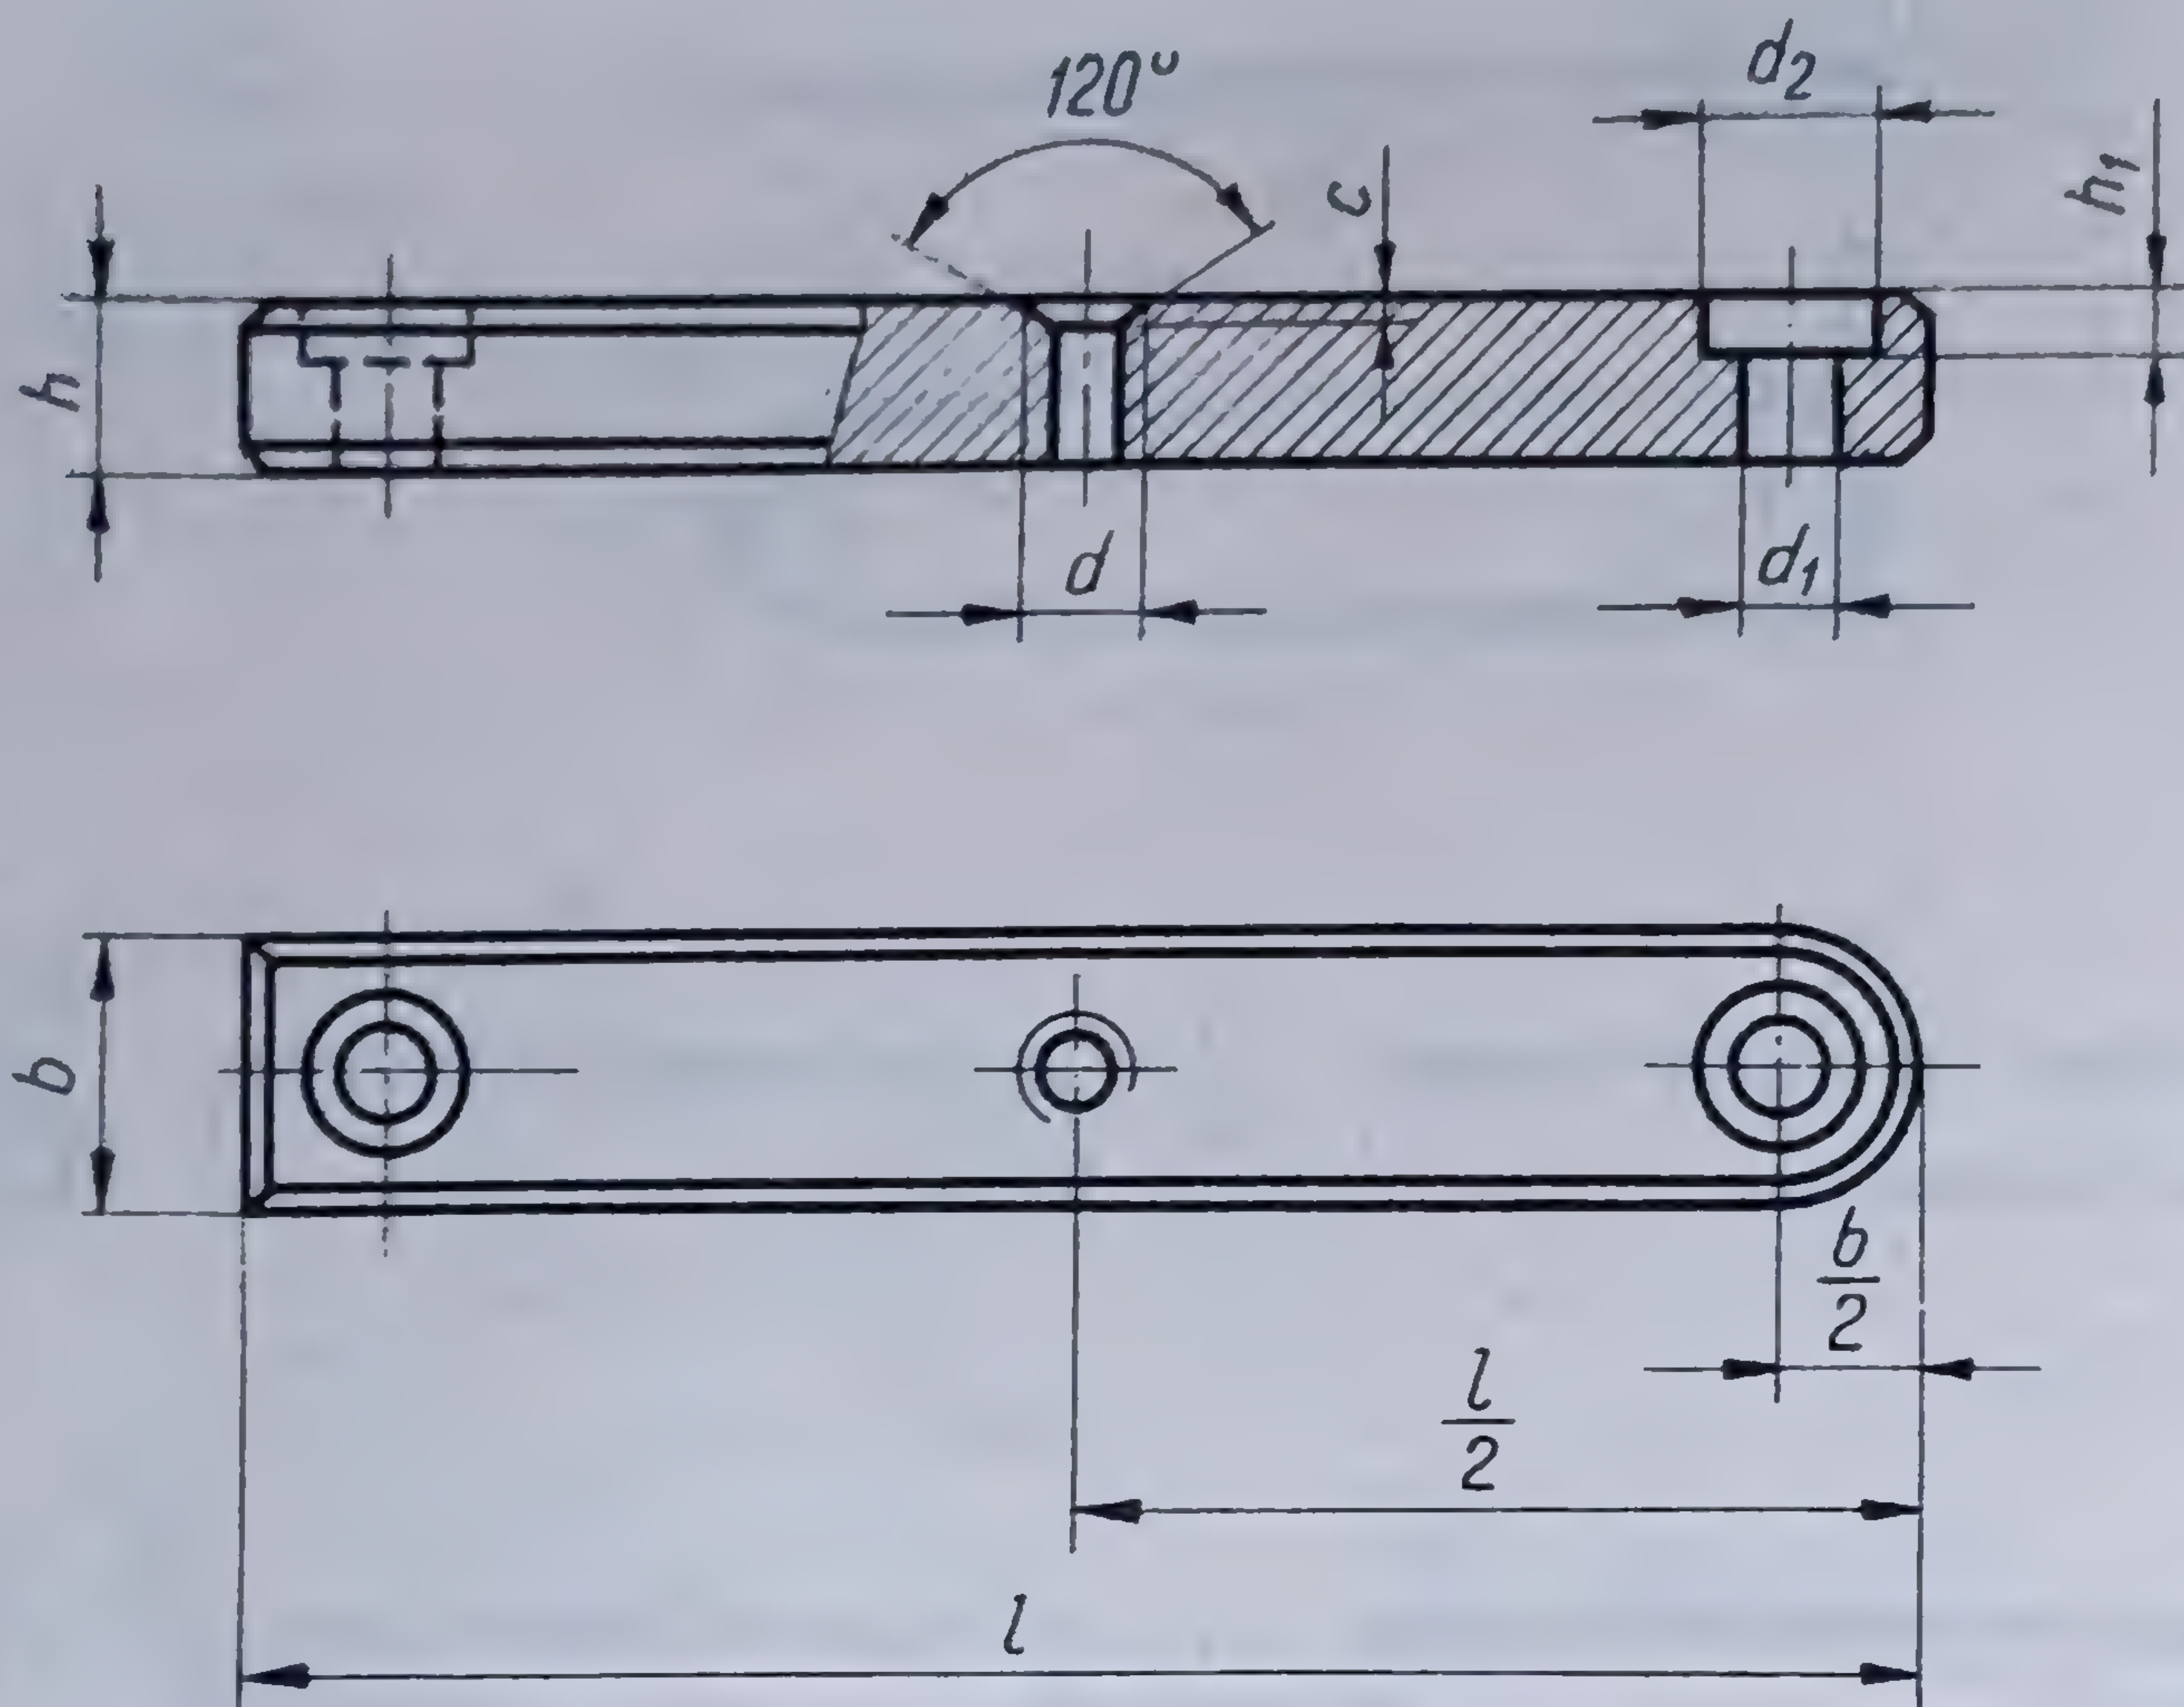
Pană paralelă cu capete rotunde (formă A)
